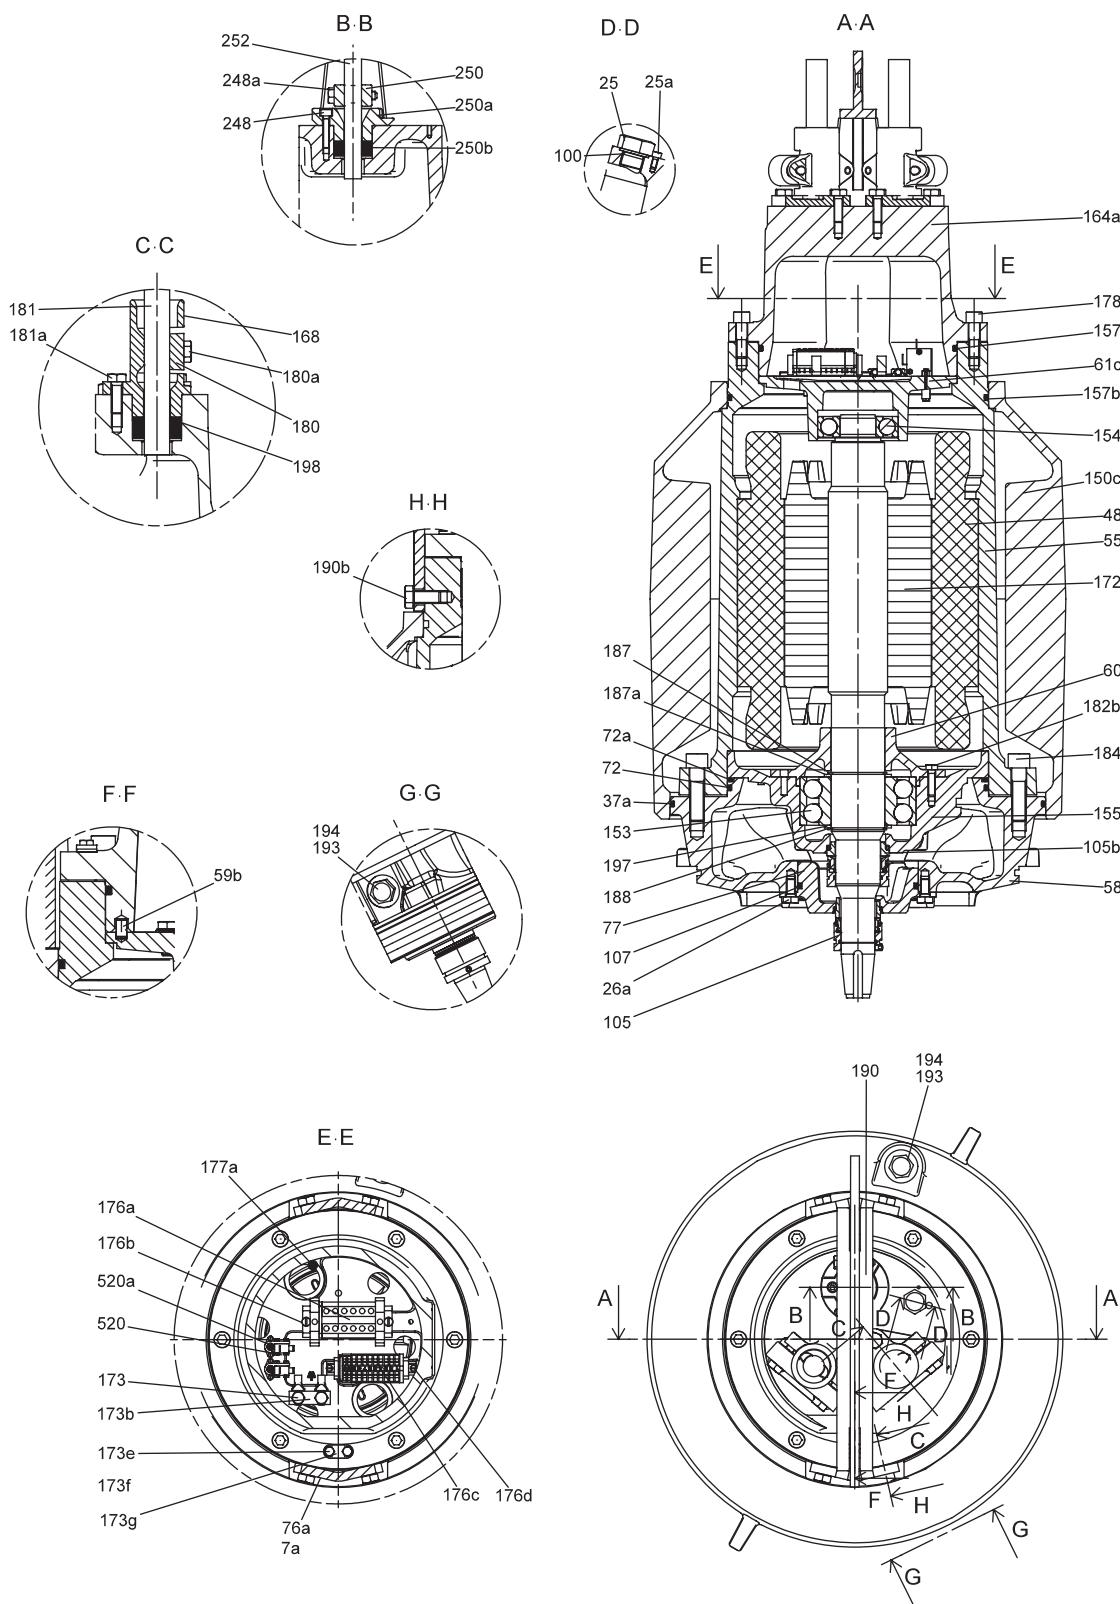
Взрывозащищённый двигатель с охлаждающим кожухом
